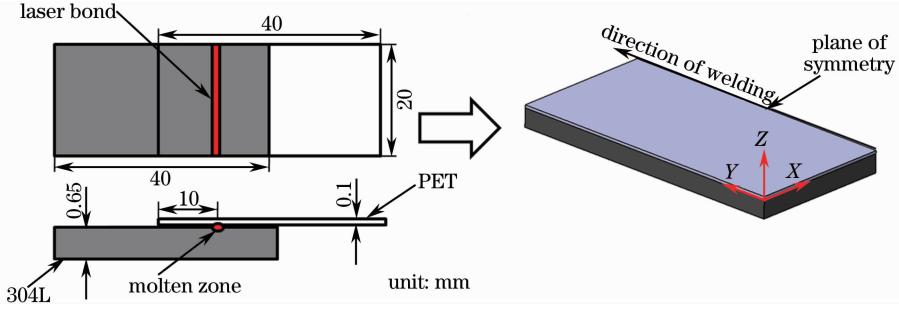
焊接样品的尺寸图与搭接部分一半的尺寸图
